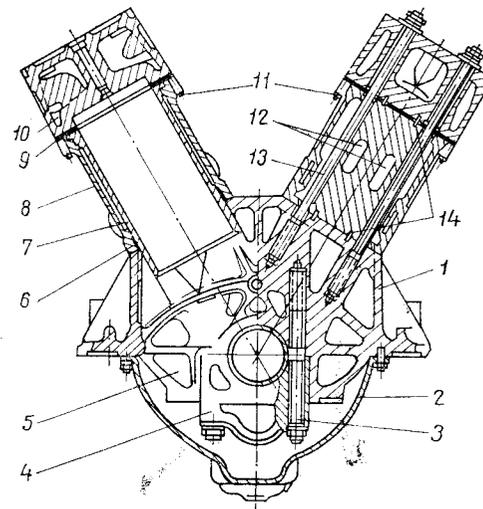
Схема картера силовая с блоками: 1 — картер верхний; 2 — картер нижний; 3 — шпилька силовая; 4 — подвеска; 5 — упор боковой; 6 — кольцо резиновое; 7 — гильза цилиндра; 8 — рубашка блока; 9 — прокладка головки блока; 10 — головка блока; 11 — шпильки шпильные; 12 — полости водяные; 13 — шпилька анкерная; 14 — штифты
